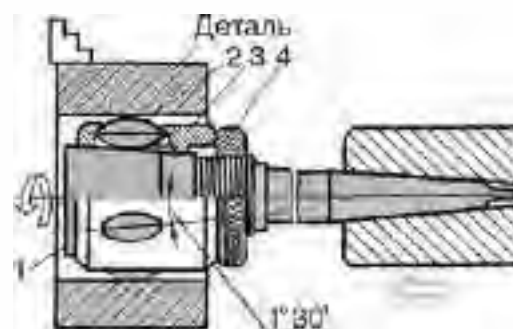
ВНУТРІШНЯ РОЗКАТКА
